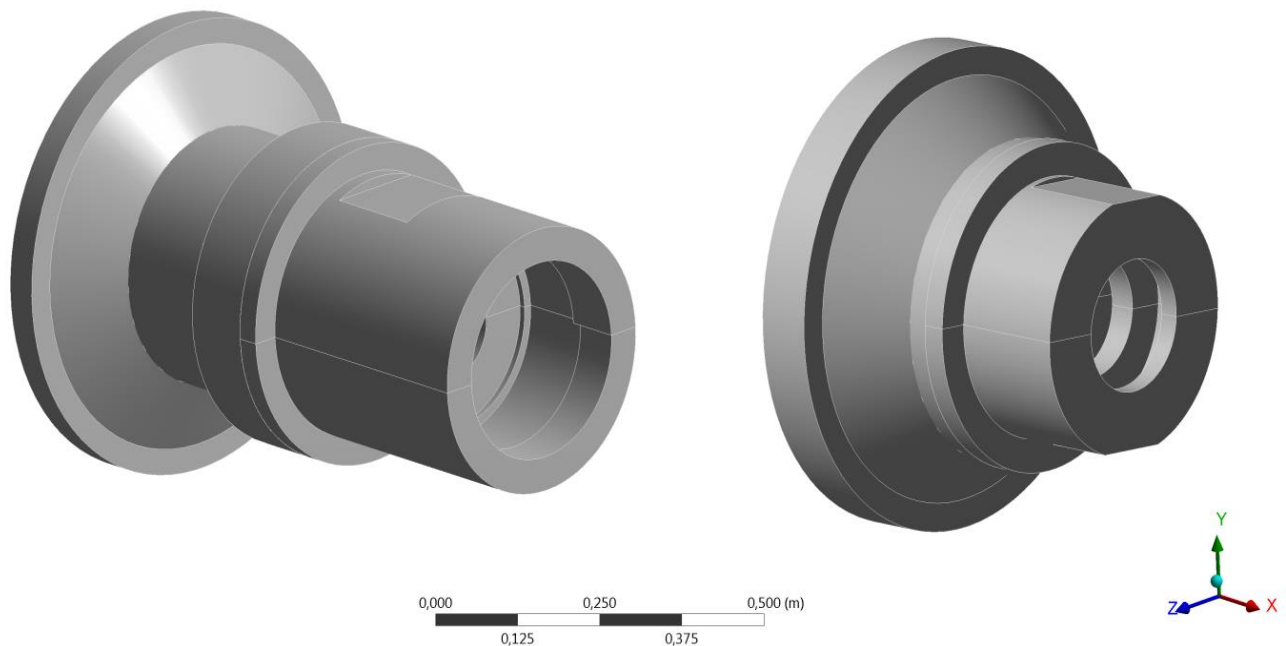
Конструкції корпусів підшипникових опор живильного насоса
